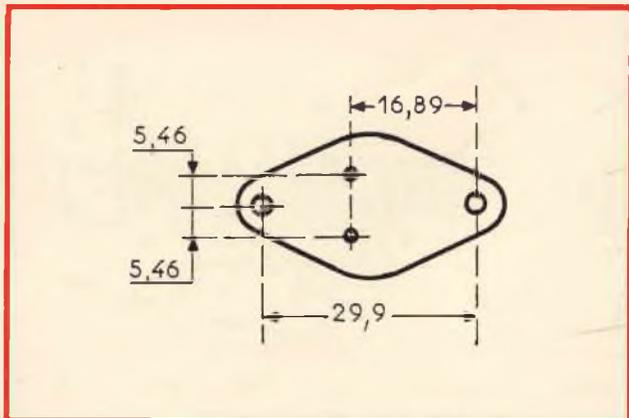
Foratura della piastrina per il montaggio del transistor.
